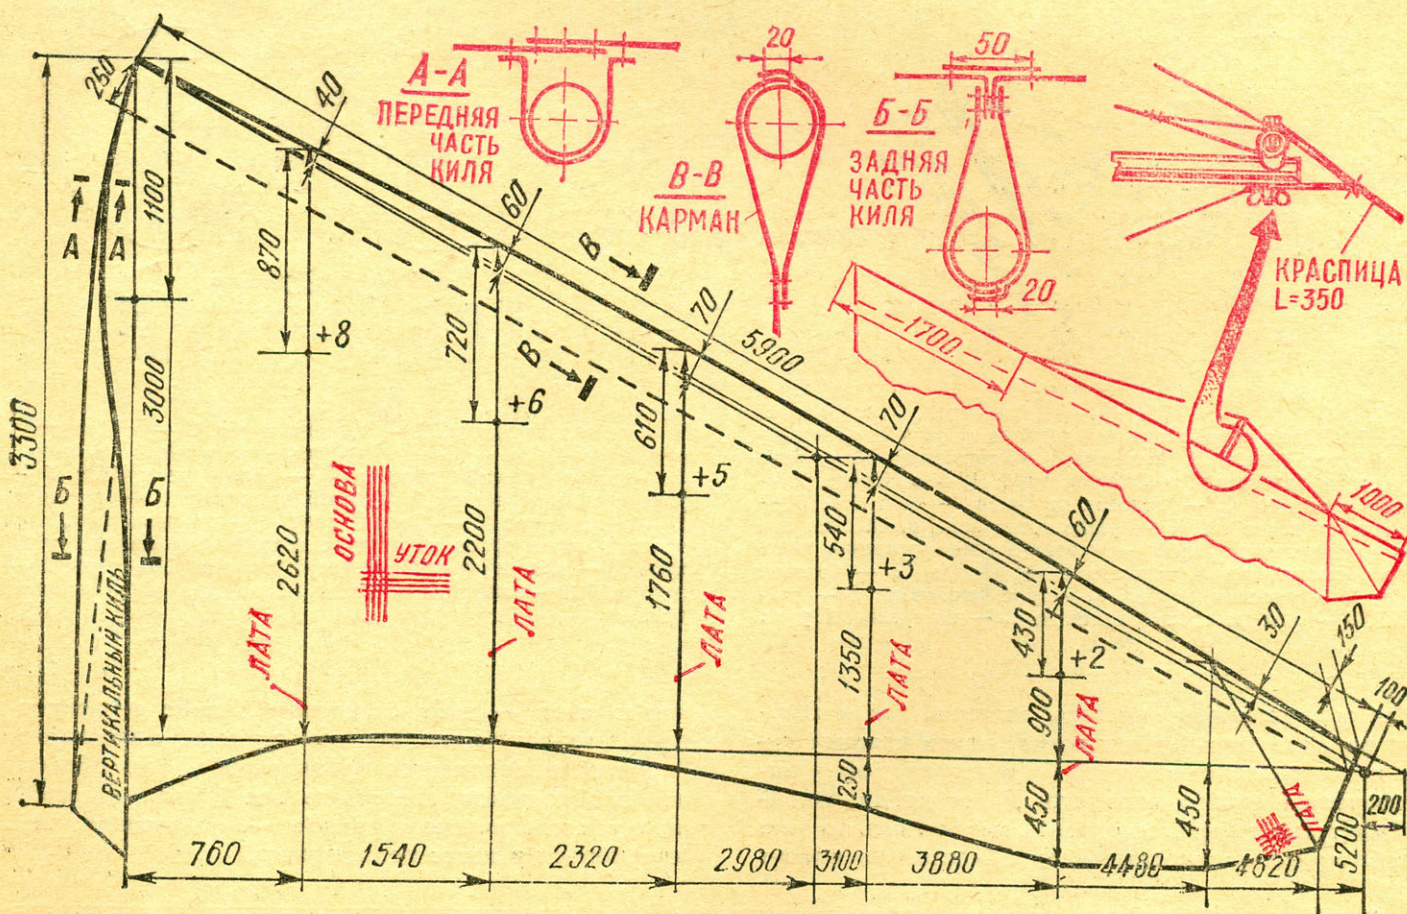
Теоретический чертеж паруса и конструкция основных швов.
